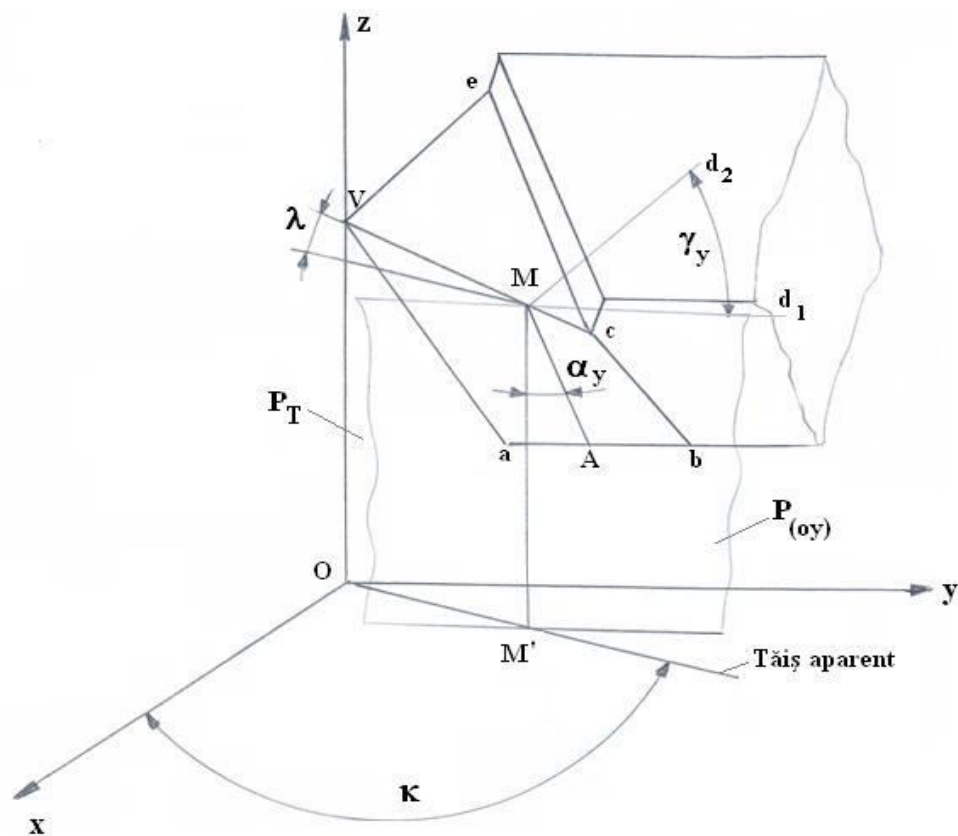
b Reprezentarea spațială a parametrilor geometrici constructivi (măsurăți în plan transversal la tăișul aparent) ai unui dinte elementar de sculă
